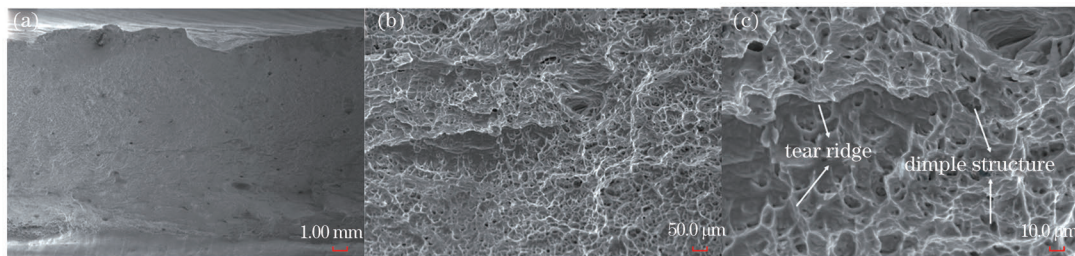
拉伸断口的截面及韧窝结构。(a)拉伸断口截面;(b)图(a)的局部放大图;(c)撕裂棱和韧窝结构
